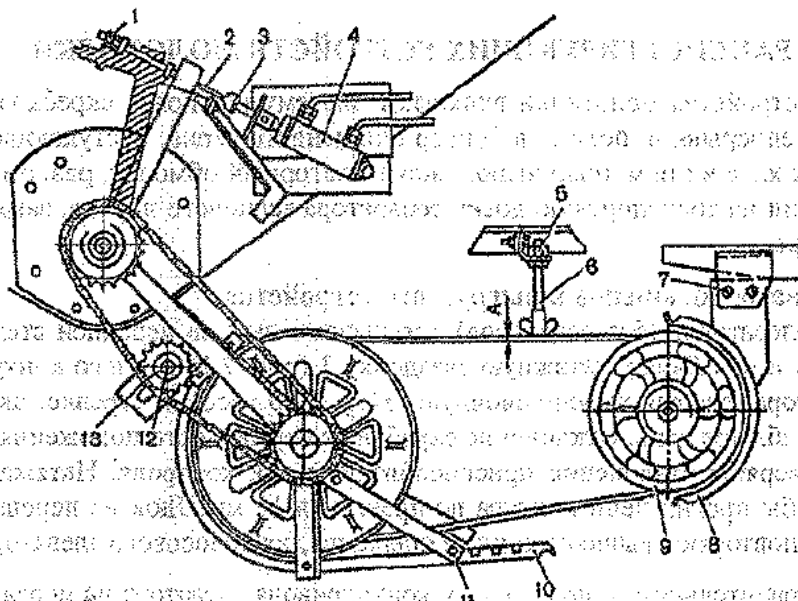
Регулировка механизма включения выгрузного устройства:
